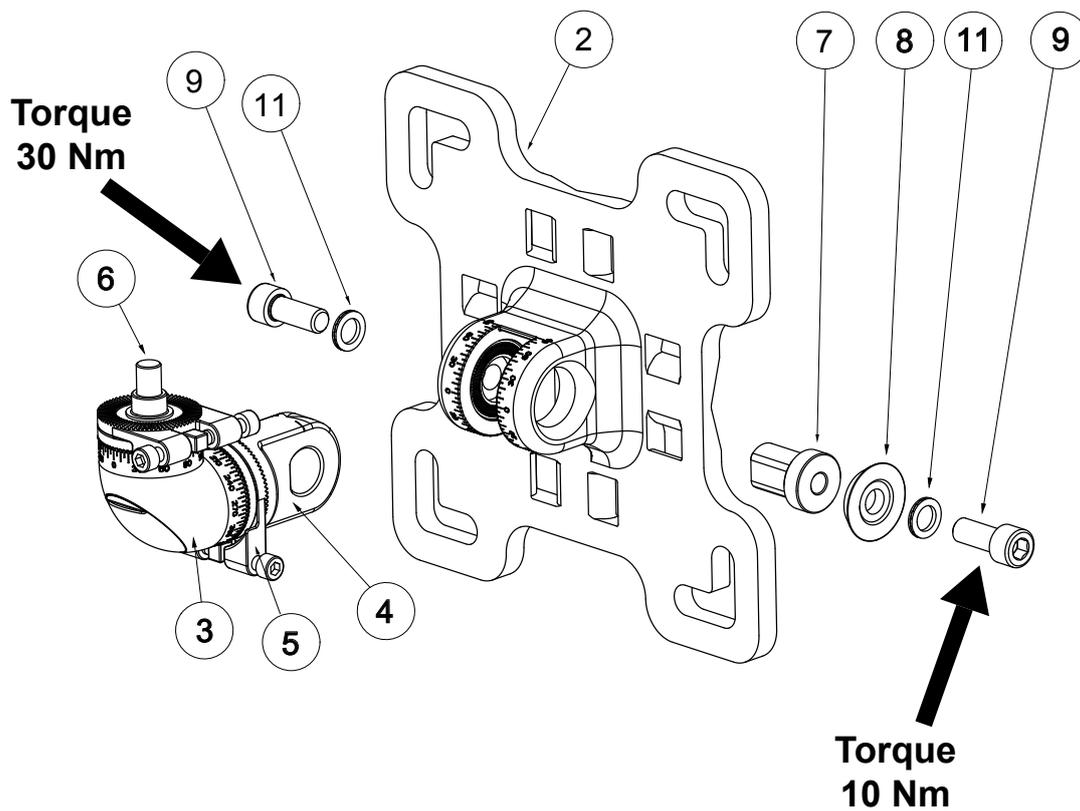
Mudança do adaptador de placa de montagem para o suporte de montagem universal
